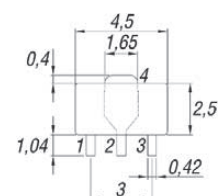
Pinbelegung (SOT-89) und Gehäuseabmessungen (nicht maßstäblich)
